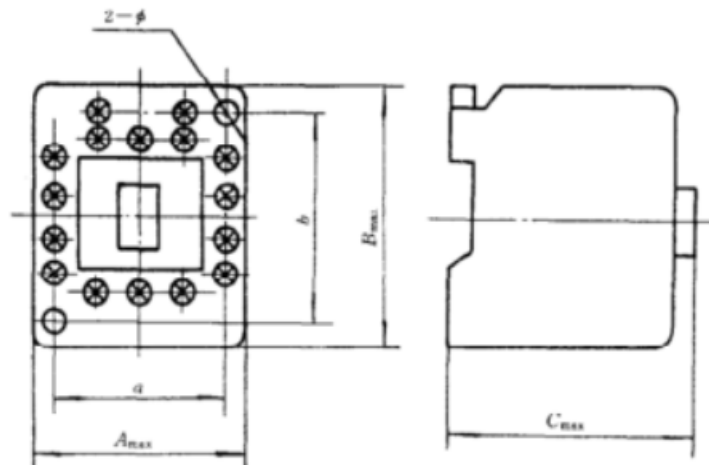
CJX 5-50~105 型交流接触器外形尺寸与安装尺寸
